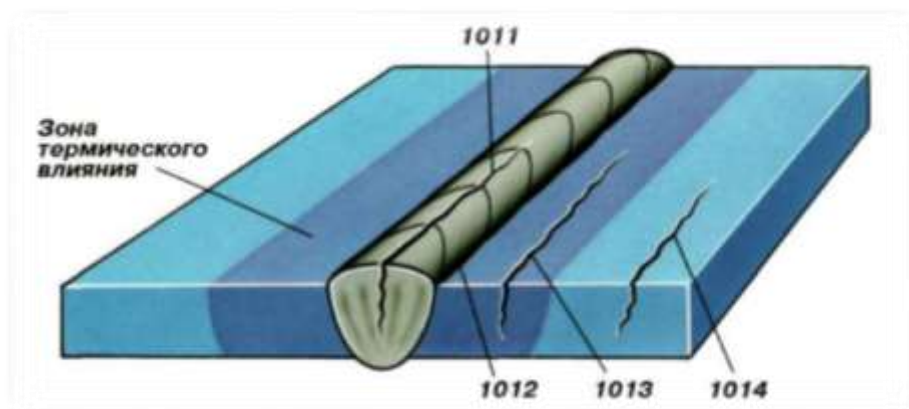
Дефекты сварного шва по типу продольных трещин
